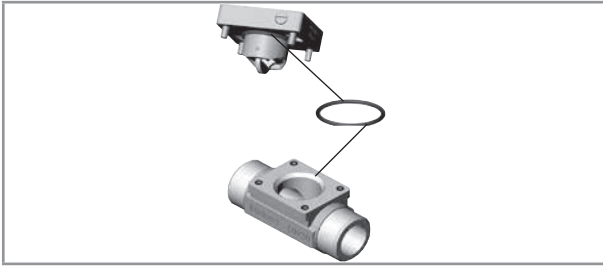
Dichtungsposition bei einem Fitting S030 HT
